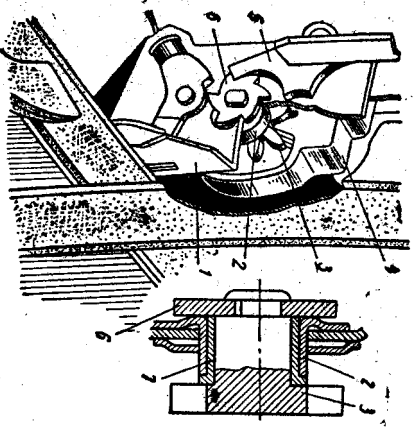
Установка замка двери: 1 — кнопка наружной ручки; 2 — направляющие штифы; 3 — ротор замка; 4 — подвижной сухарь фиксатора; 5 — фиксатор двери.
